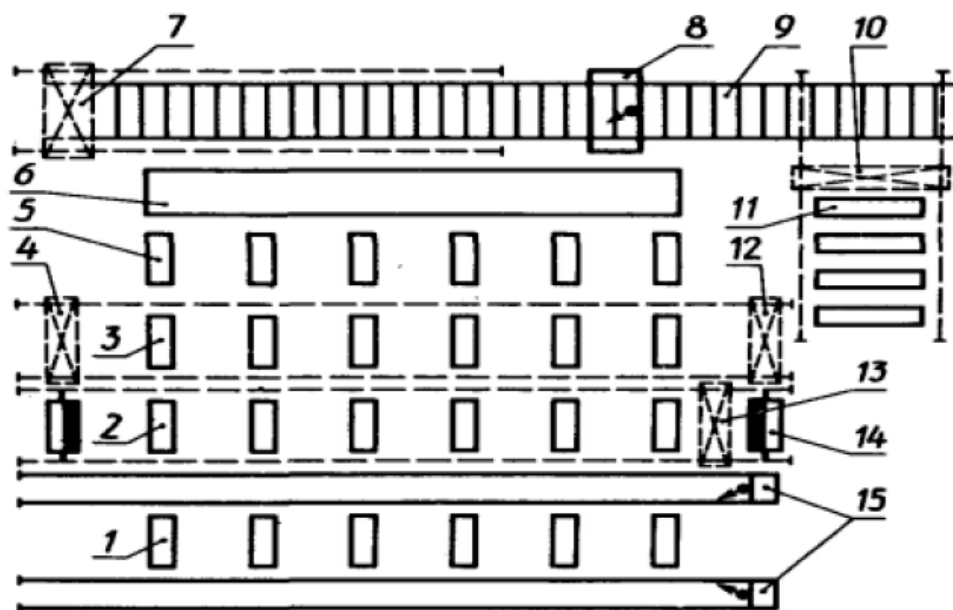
Поточна лінія виготовлення балок коробчастого перерізу: 1 – стенд для зварювання поясних швів; 2 – стенд остаточного складання; 3 – стенд для прогинання балки; 4 – портална самохідна установка для складання стінок; 5 – стенд для складання та зварювання верхнього пояса з діафрагмами; 6 – накопичувач; 7 – ділянка рентгенівського контролю; 8 – зварювальний стенд; 9 – роликовий конвеєр; 10 – порталний кран; 11 – склад оброблених заготовок; 12 – портална установка для зварювання діафрагми зі стінками; 13 – самохідний портал; 14 – гідродомкрат; 15 – зварювальний автомат.
